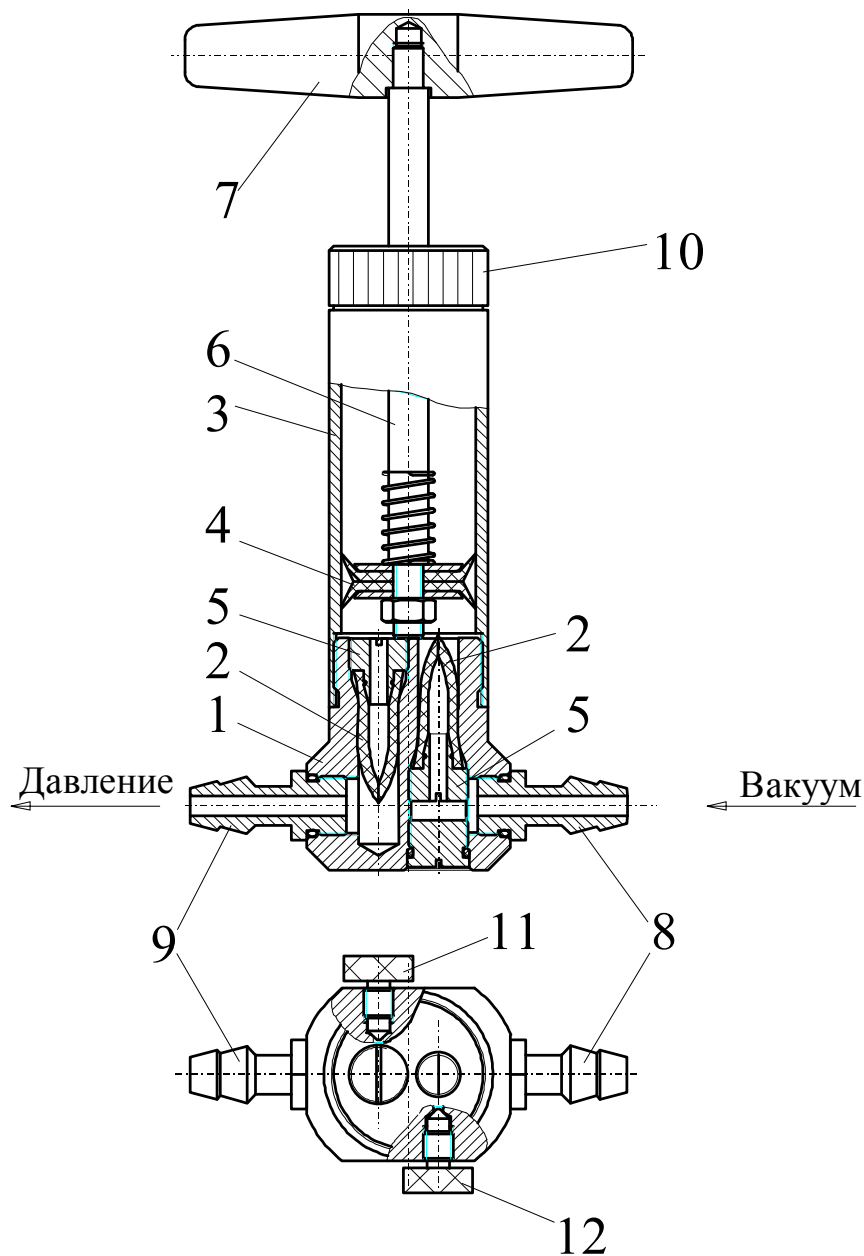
Конструктивная схема насоса ручного универсального НУР5: 1 - корпус; 2 - обратный клапан резиновый; 3 - гильза; 4 - поршень; 5 - ниппель; 6 - шток; 7 - ручка; 8 - штуцер вакуумный; 9 - штуцер напорный; 10 - крышка; 11 – вентиль выпуска воздуха; 12 - вентиль напуска воздуха.
